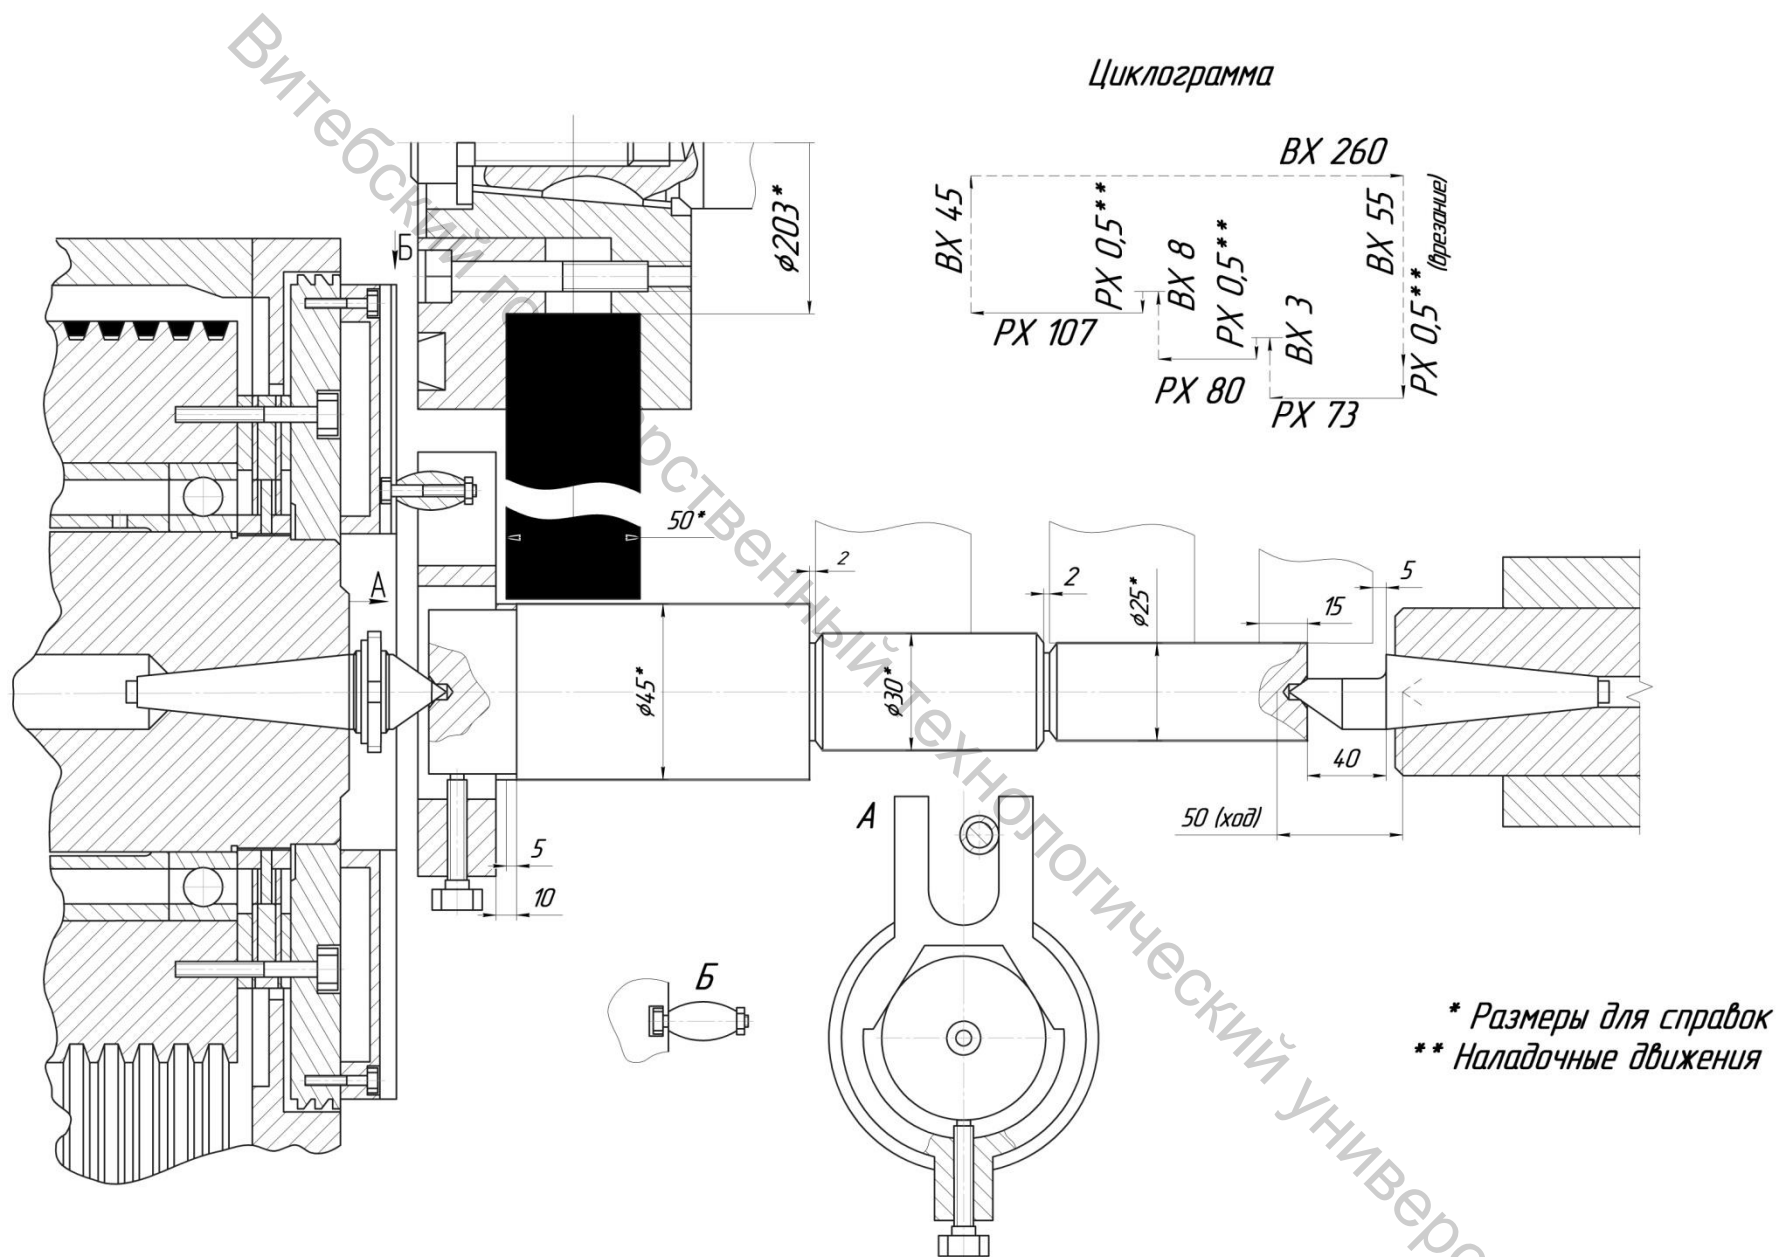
Схема наладки станка ЗМ153П на операцию круглого шлифования заготовки детали «Вал»
